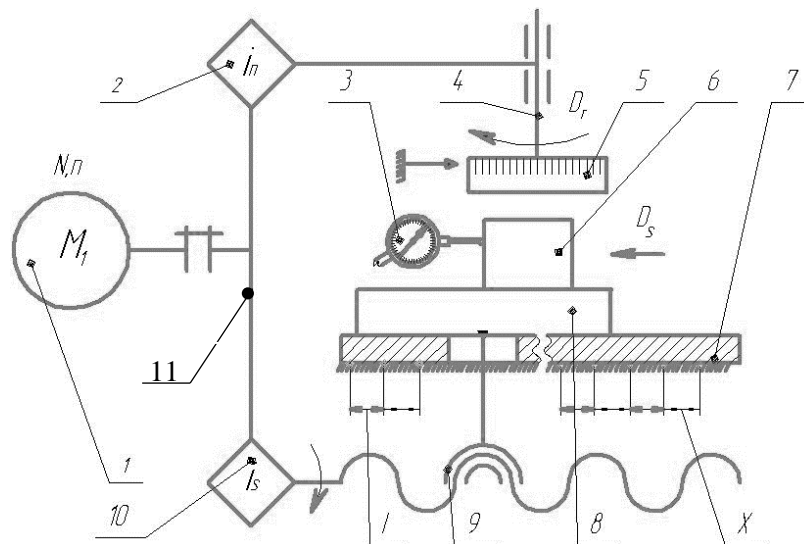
Схема вимірювання величини подачі на зуб фрези:
